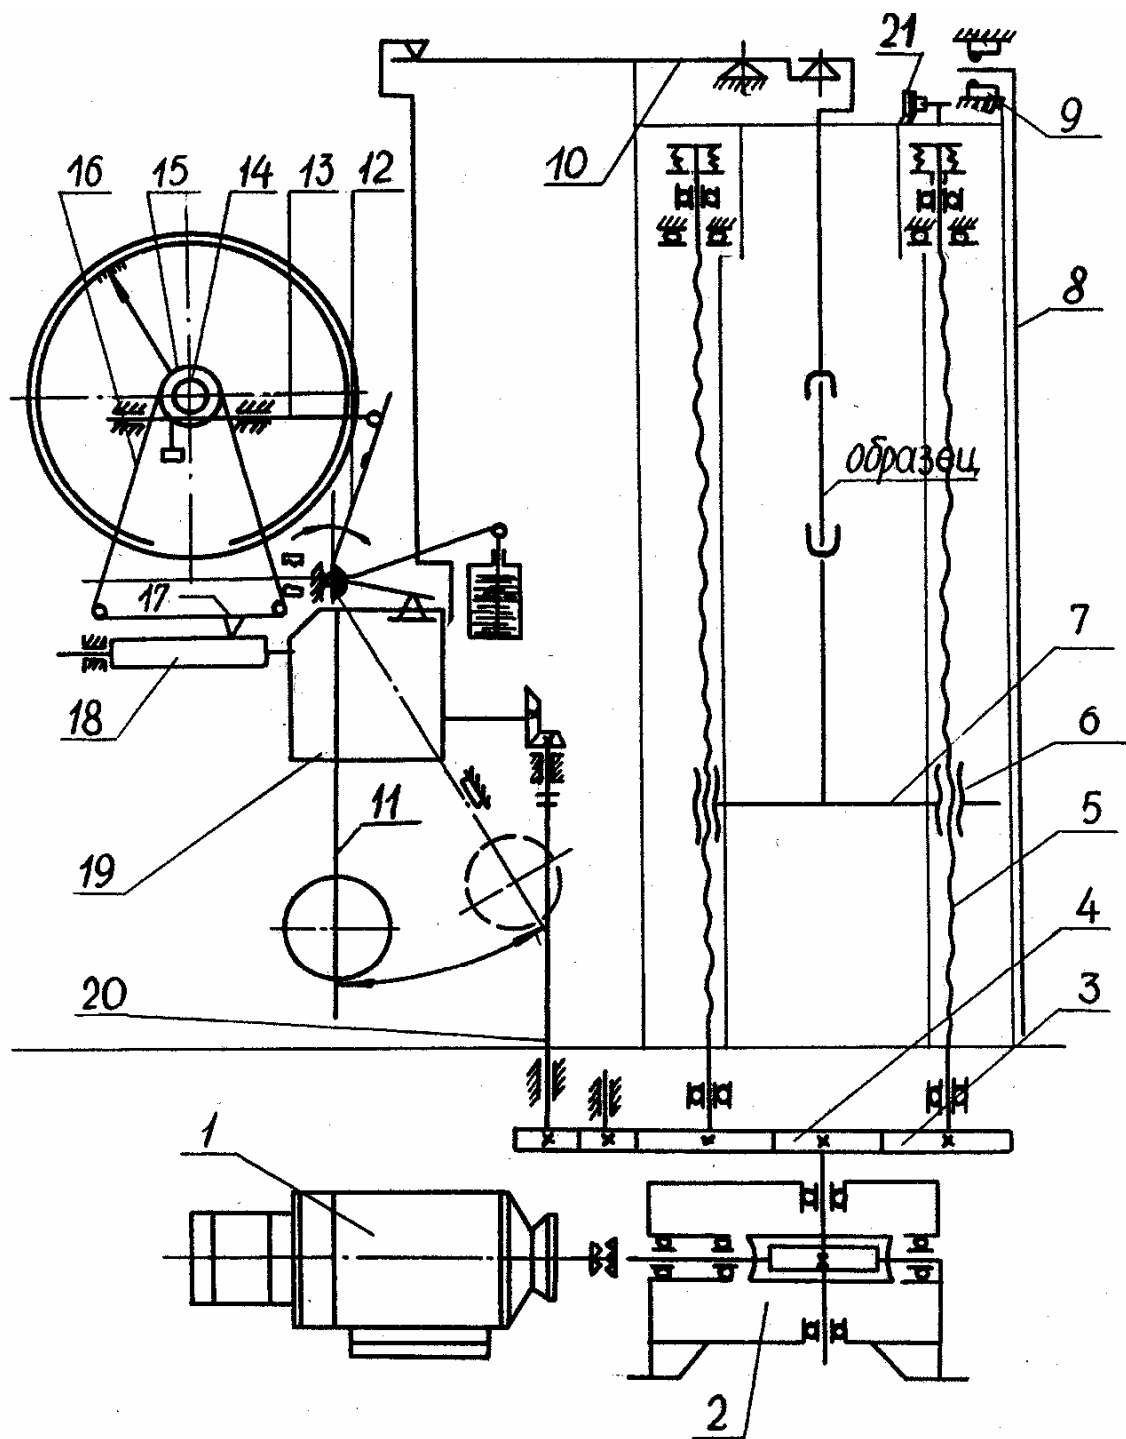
1 — двигатель; 2 — редуктор; 3, 4 — шестерни; 5 — винт; 6 — гайки; 7 — подвижная траверса; 8 — шток; 9 — микровыключатели; 10 — рычаг силоизмерителя; 11 — маятник; 12 — поводок; 13 — зубчатая рейка; 14 — шестерня; 15 — шкив; 16 — гибкий тросик; 17 — перо самопишущего прибора; 18 — барабан лентопротяжного механизма; 19 — масштабный преобразователь; 20 — шарнирный валик
